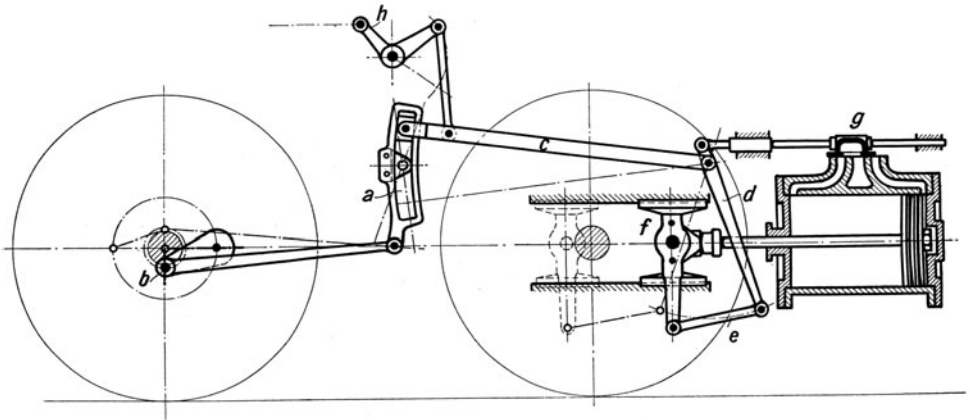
Heusinger-Steuerung einer Druckluftlokomotive.
